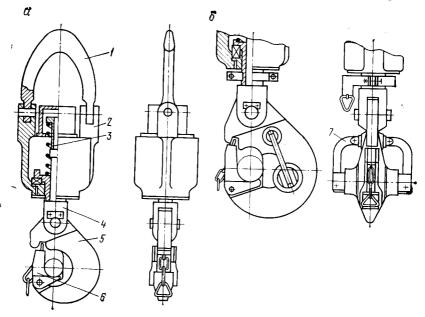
Подъемные крюки: - исполнение I; б— исполнение II; f— серьга; 2— корпус крюка; f— пружина; f— ствол крюка; f— рог крюка; f— седло; f— дополнительный рог со скобой
